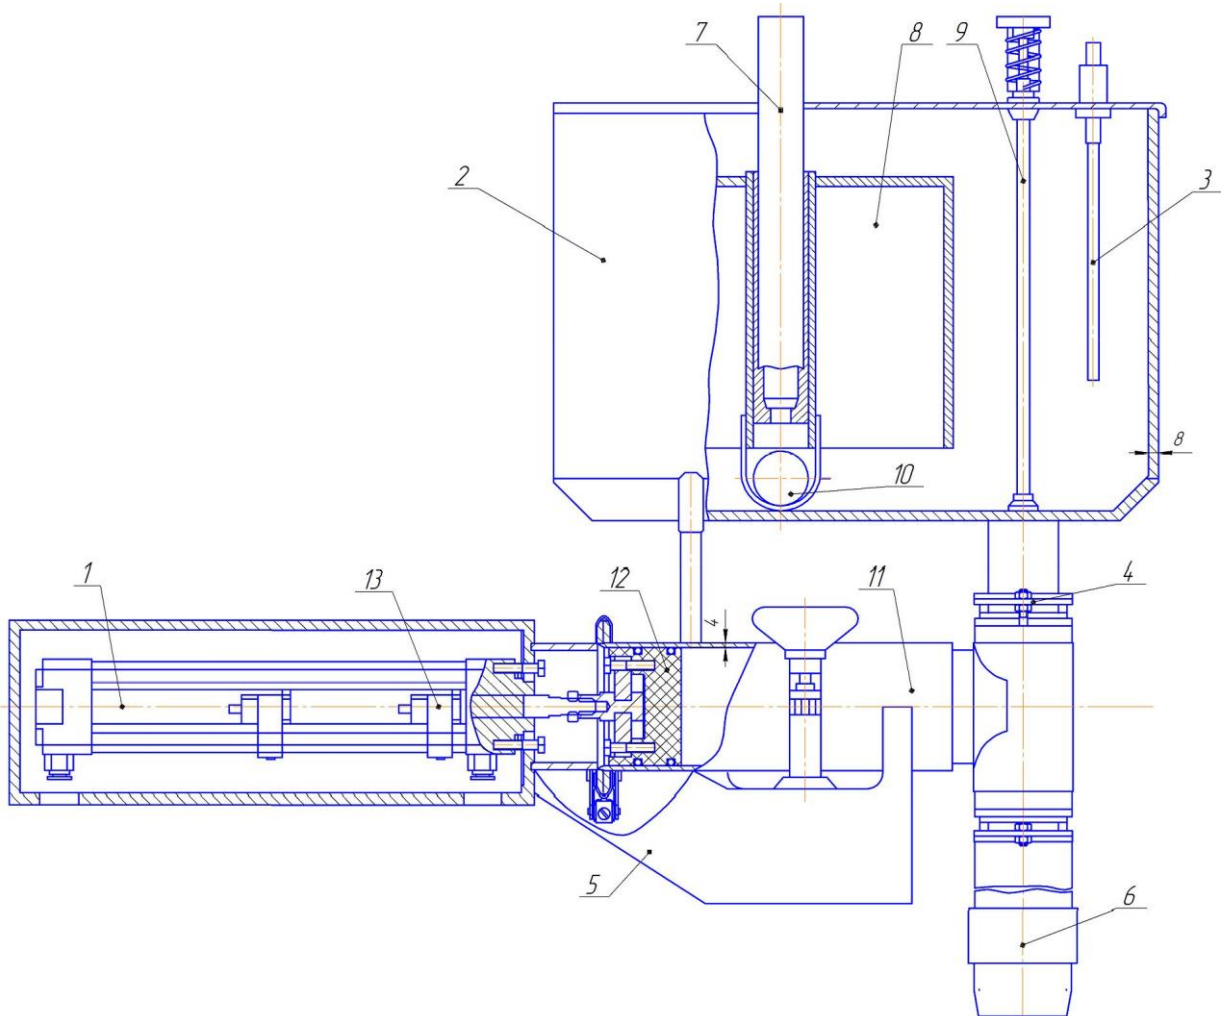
Поршневий дозатор: 1 – пневмоциліндр; 2 – бачок для молока; 3 – датчик; 4 – верхній клапан; 5 – корпус; 6 – нижній клапан; 7 – трубопровід для подачі молока; 8 – поплавков; 9 – трубка для випуску повітря; 10 – кулька; 11 – гільза; 12 – поршень; 13 – магнітний датчик
